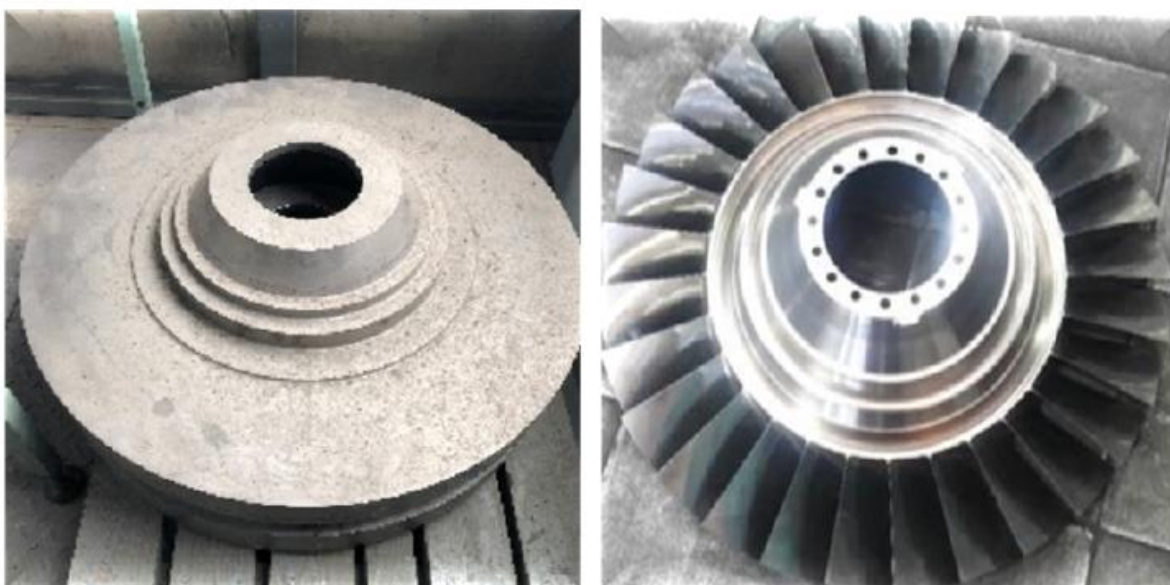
Фото заготовки и моноколеса второй ступени КНД ГТД
